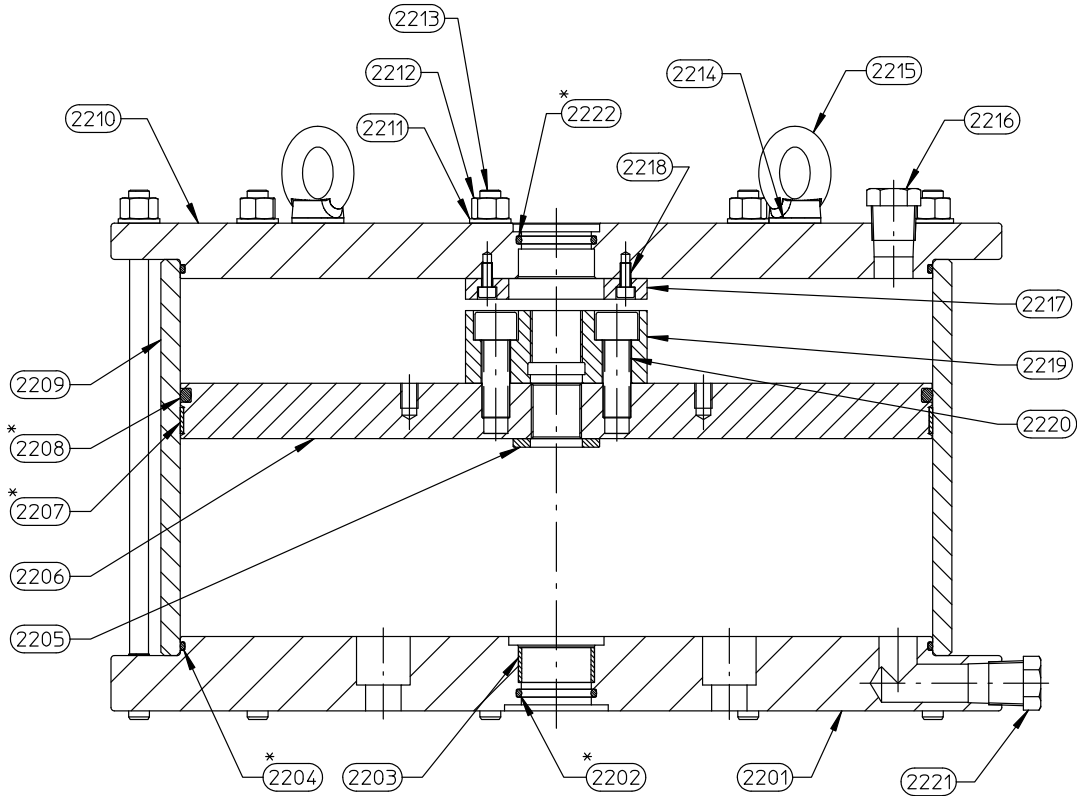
Пневматический цилиндр привода Fisher 785C в сборе с ручным дублиром верхнего монтажа, беспружинный или пружинный возврат, одинарное или двойное действие
